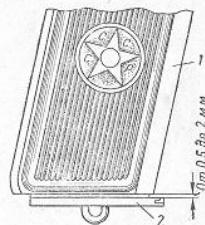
Допускаемый зазор между нижней поверхностью рукоятки и крышкой магазина:
